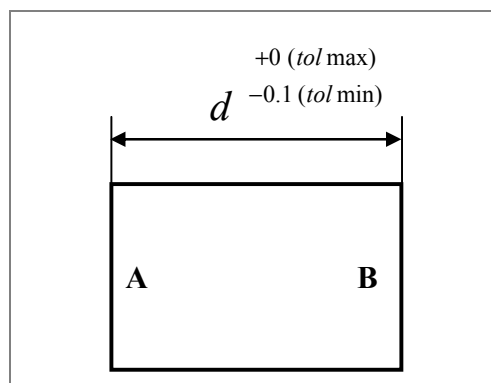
Exemple de tolérancement dimensionnel pour la pièce 1 du mécanisme
